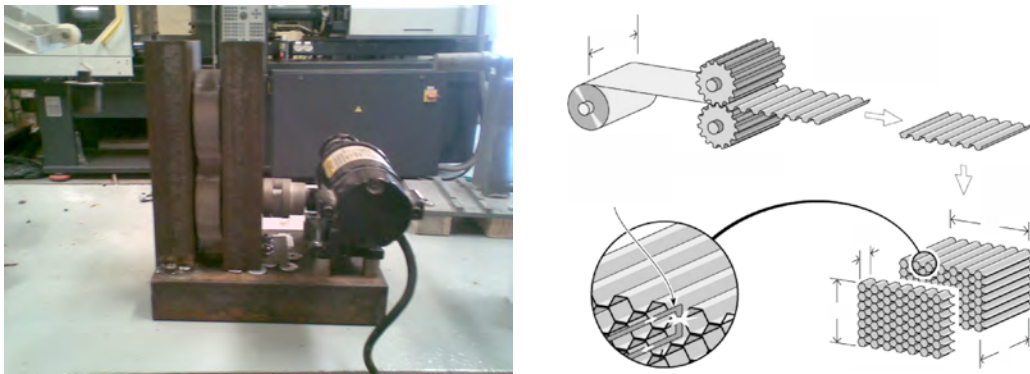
Prototipo del sistema de engranajes para el proceso de corrugado.
